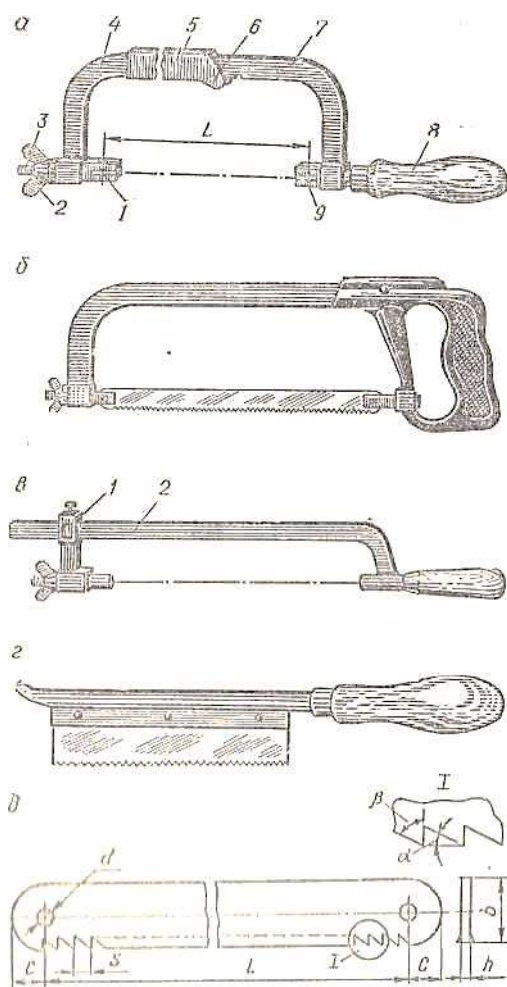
Ручные ножовки и ножовочное полотно
